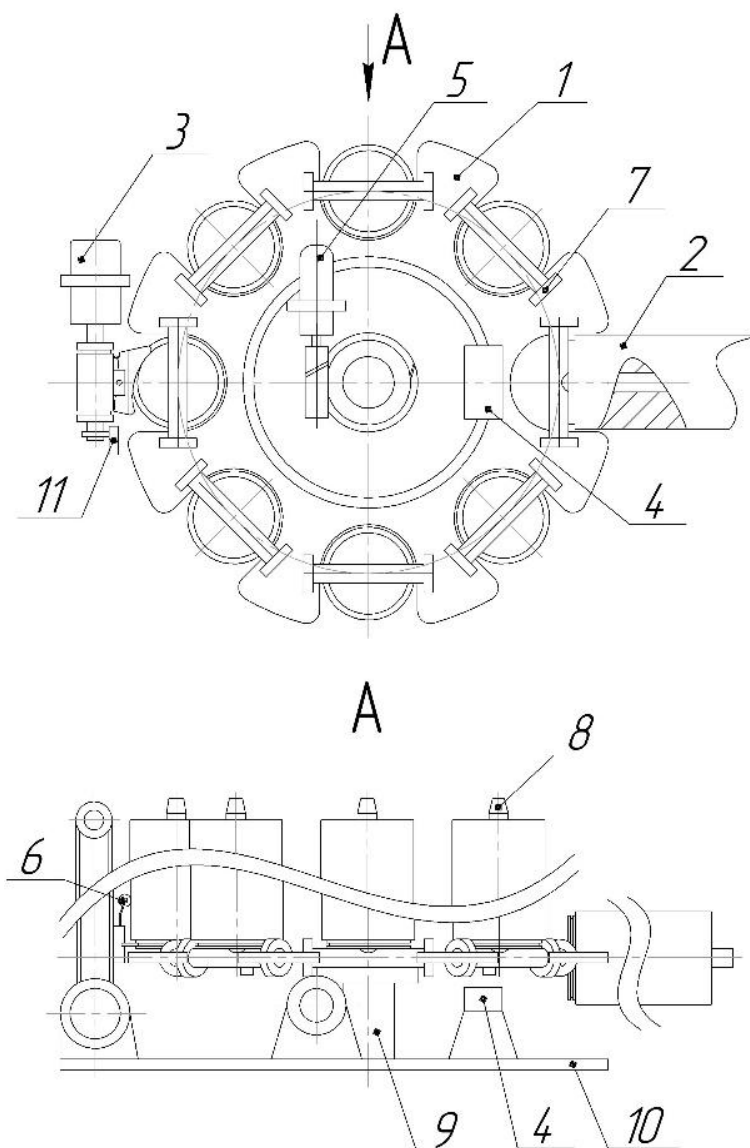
Схема устройства револьверной замены печатных форм для флексографской печати: 1) барабан с направляющими, 2) гильза с печатной формой, 3) привод подачи гильз, 4) датчик угла поворота барабана, 5) привод поворота барабана, 6) скользящий валик подающего устройства, 7) поворотные шарниры с направляющими для гильз, 8) сопрягающая резиноканевая муфта, 9) ось барабана 10) кожух барабана, 11) датчик положения подающего устройства
